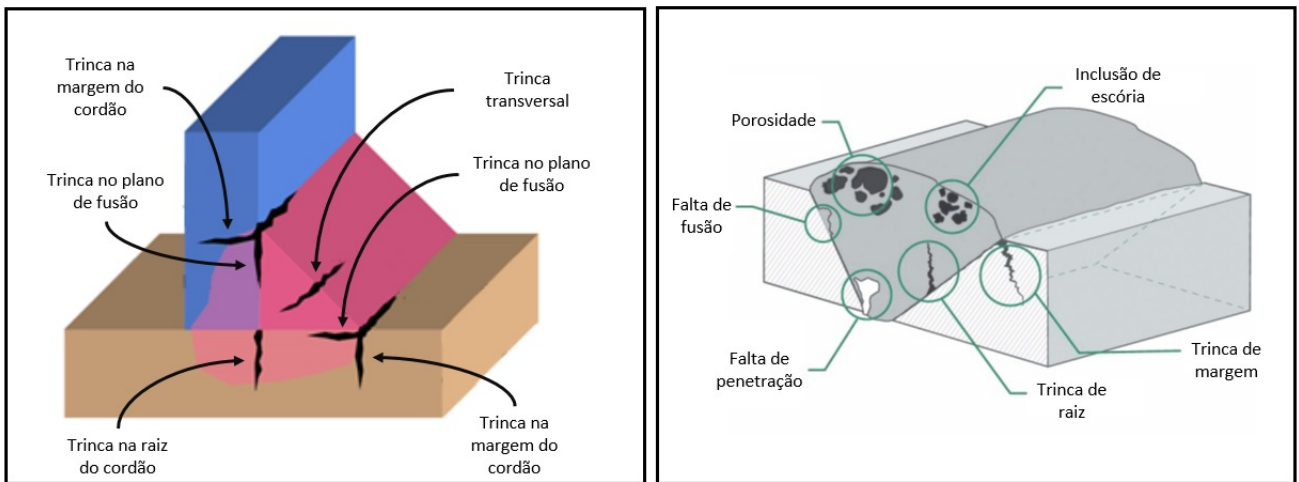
Descontinuidades em juntas soldadas. (OPTIMEC CONSULTANTS, 2014)
